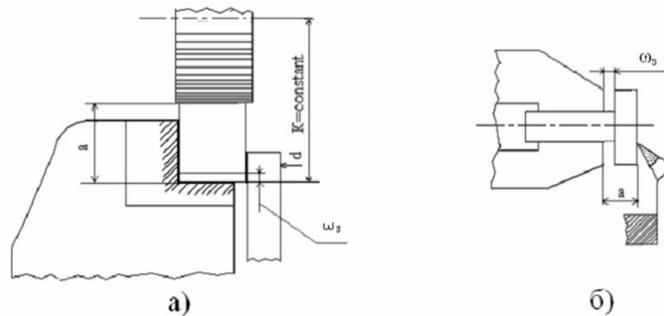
Погрешность закрепления ω_3 при фрезеровании (а) и при токарной обработке (б)
